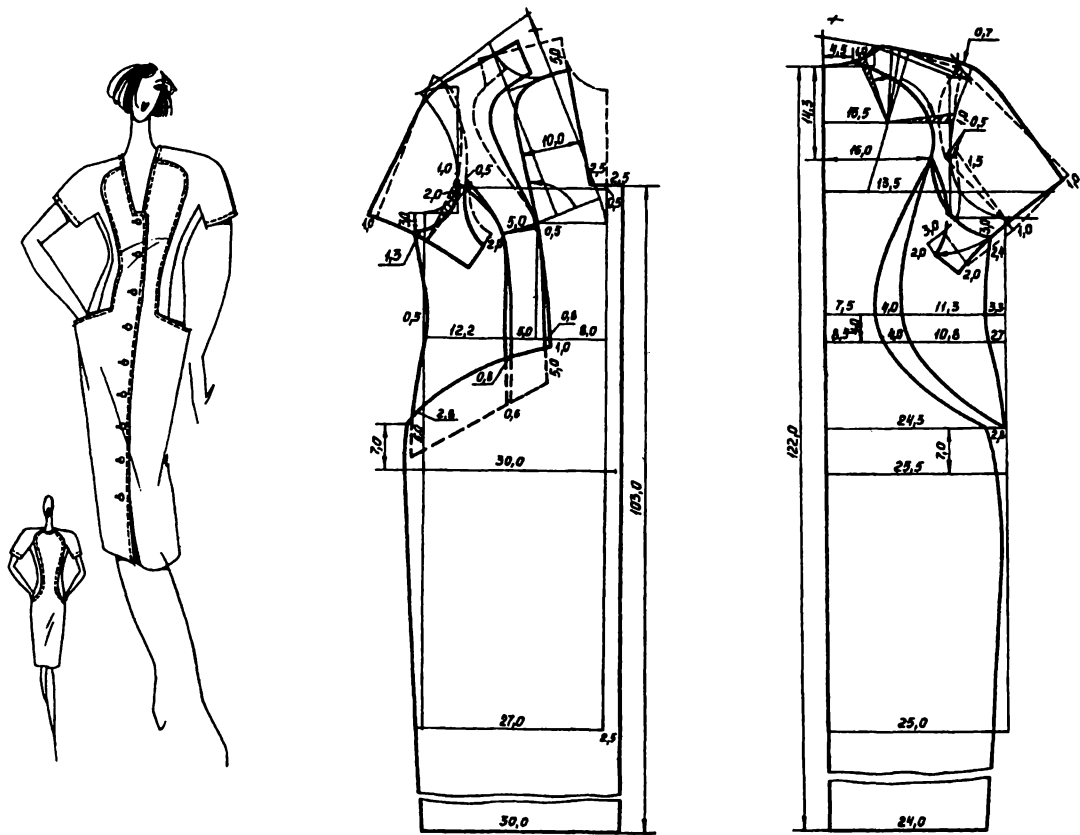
Модель и чертеж конструкции женского платья полуприлегающего силуэта
